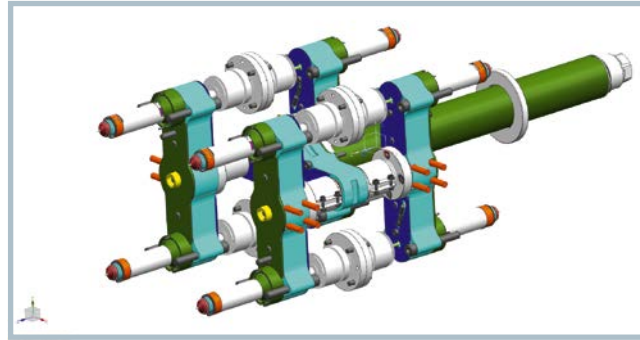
8-fach-Heißkanalsystem für das Etagenwerkzeug mit Durchführung, Verteiler und Düsen von Männer
